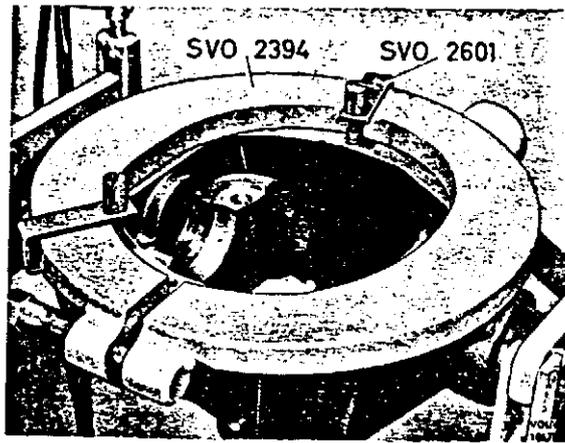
Ausspannen des Hinterachsgetriebegehäuses
